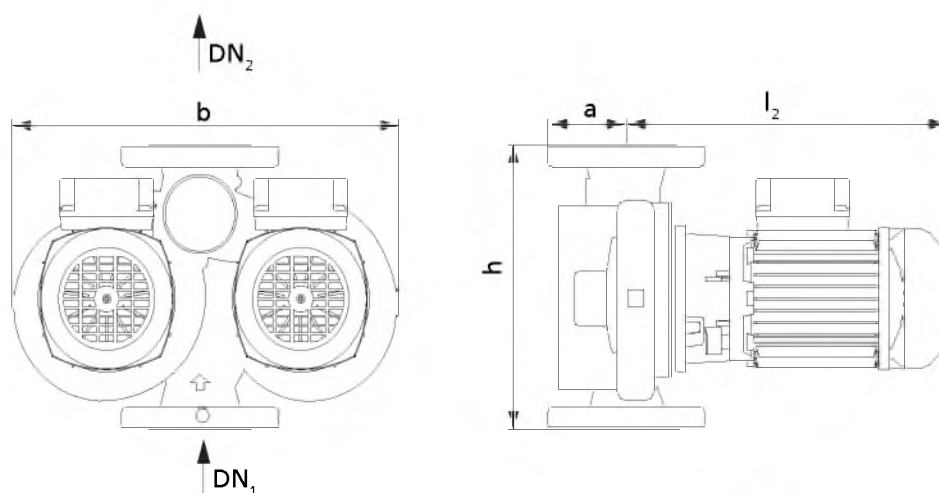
Размеры насосного агрегата с фланцевым соединением, типоразмер \geq 032-032-100
